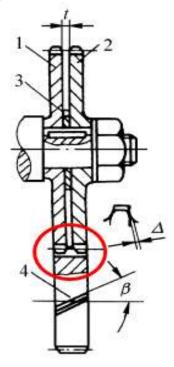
斜齿轮消隙机构 1,2-窄斜齿轮;3-垫片; 4-宽齿轮
